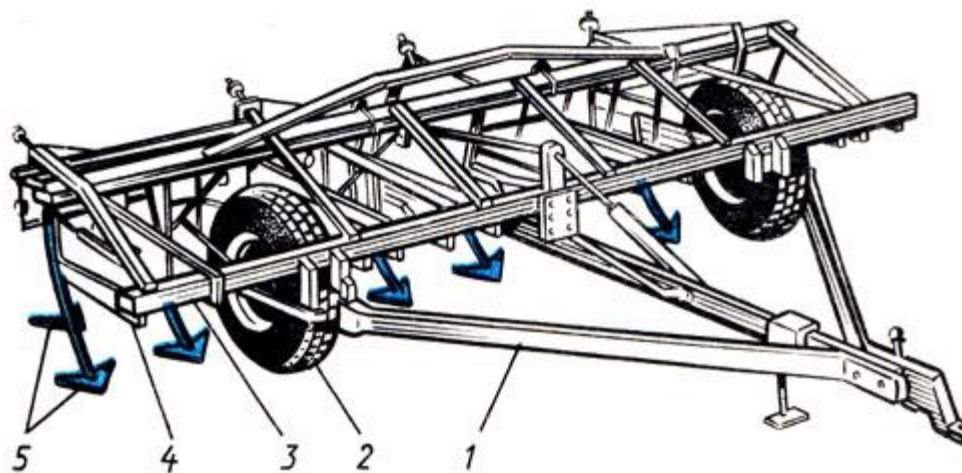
Прицепной культиватор для сплошной поверхностной обработки почвы: 1 - сница с прицепом; 2 - опорное колесо; 3 - рама; 4 - грядиль; 5 - рабочие органы (стрельчатые лапы)
